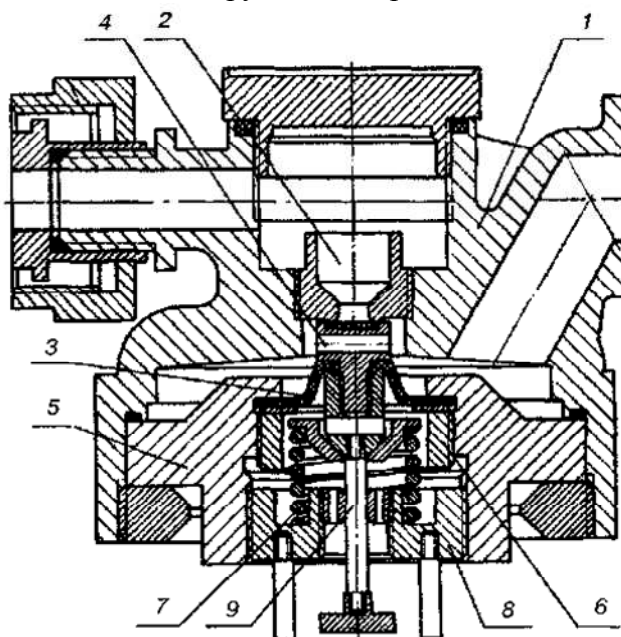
Клапан предохранительный сбросной КПС-Н:
